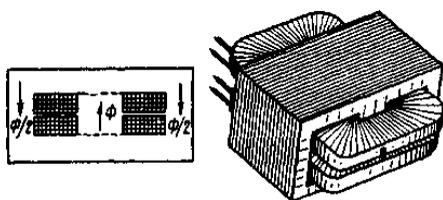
Однофазный трансформатор броневое типа: а- устройство; б- внешний вид
